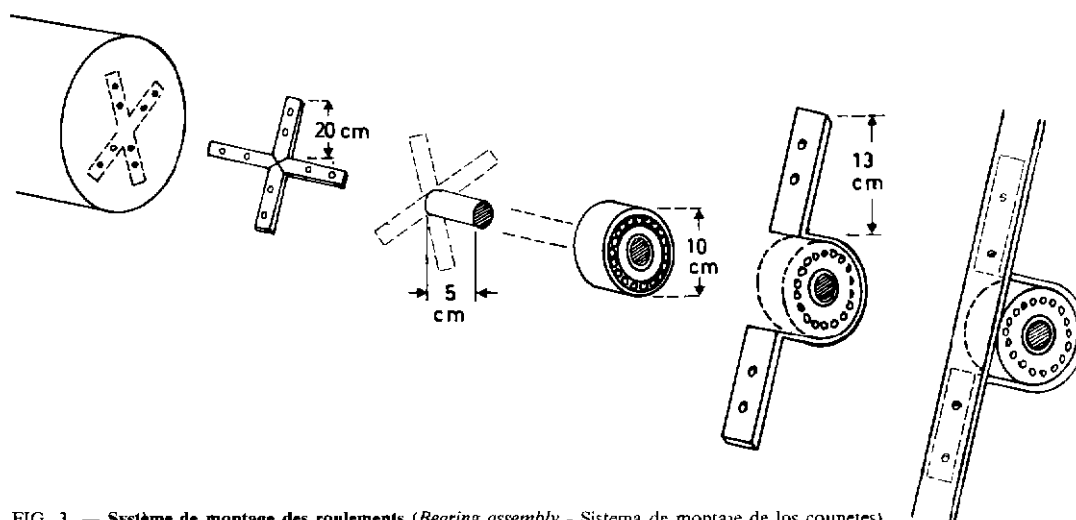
Système de montage des roulements (Bearing assembly - Sistema de montaje de los cojinetes)
